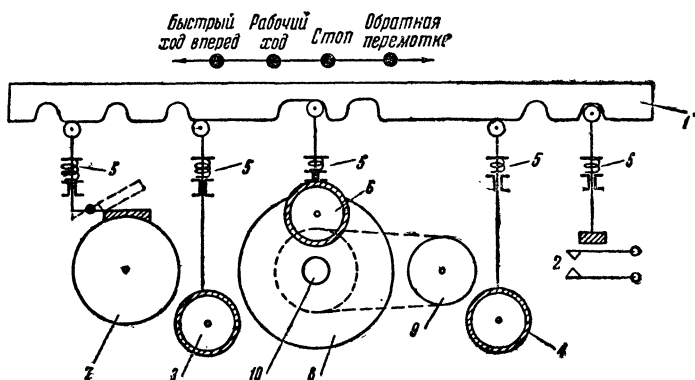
Управление одномоторным механизмом с применением паразитных обрезиненных роликов: 1 — управляющая планка; 2 — контакты включения двигателя; 3, 4 — паразитные обрезиненные ролики; 5 — возвратные пружины; 6 — прижимной ролик; 7 — шкив левой кассеты; 8 — шкив ведущего двигателя; 9 — фрикцион правой кассеты; 10 — ведущий ролик
